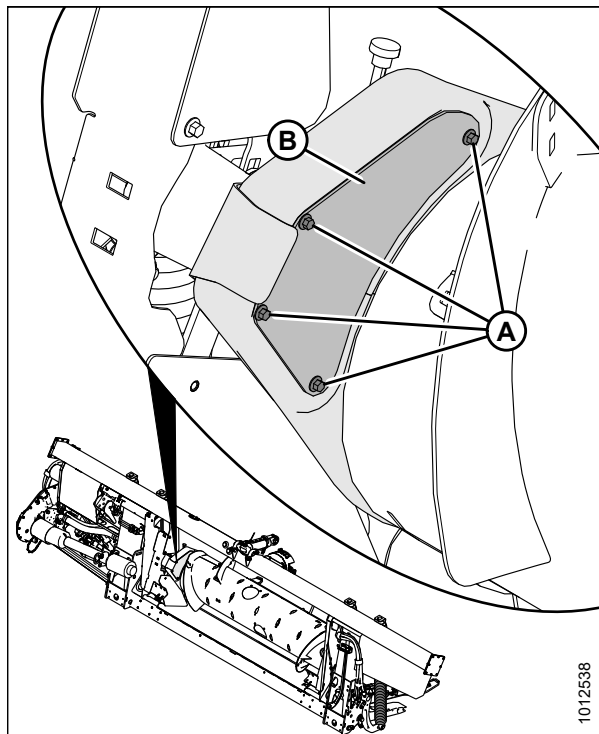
Linke Seite des Einzugstrommelgetriebes – Rückansicht
